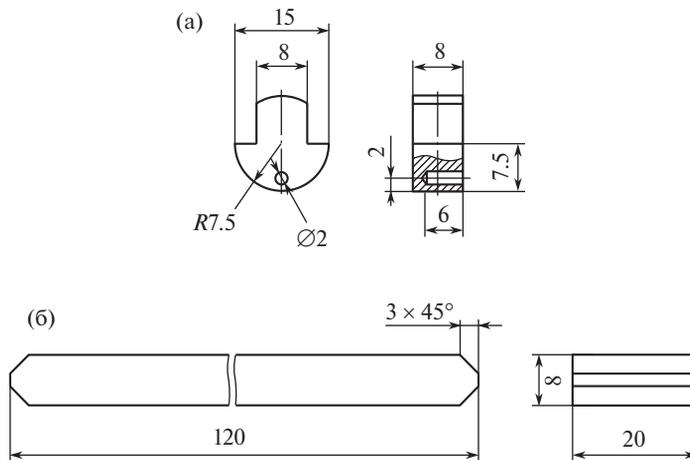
Схемы образцов: (а) – подвижный образец; (б) – неподвижный образец.
